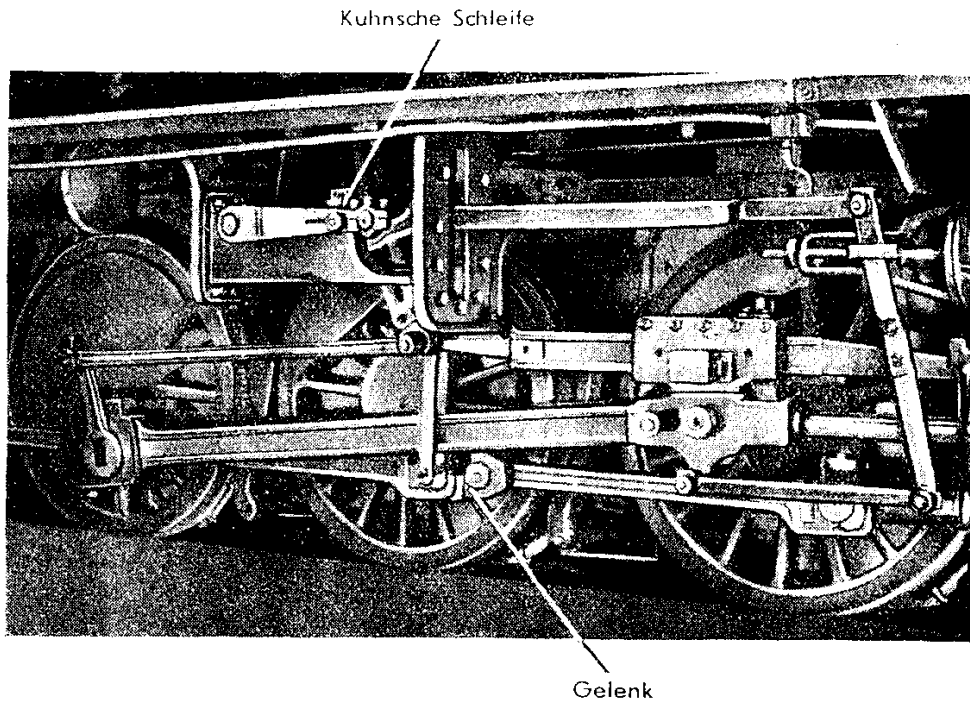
Heusinger-Steuerung mit Kuhnscher Schleife
